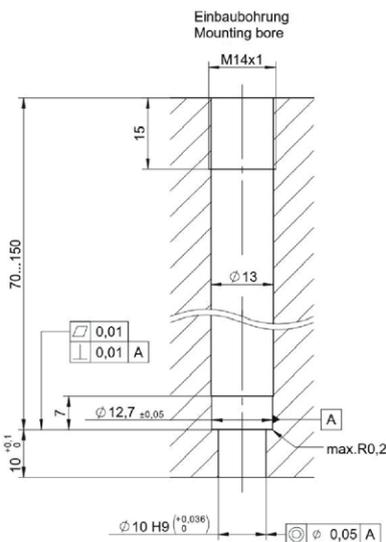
Einbaubohrung bei brennraumbündiger Montage
